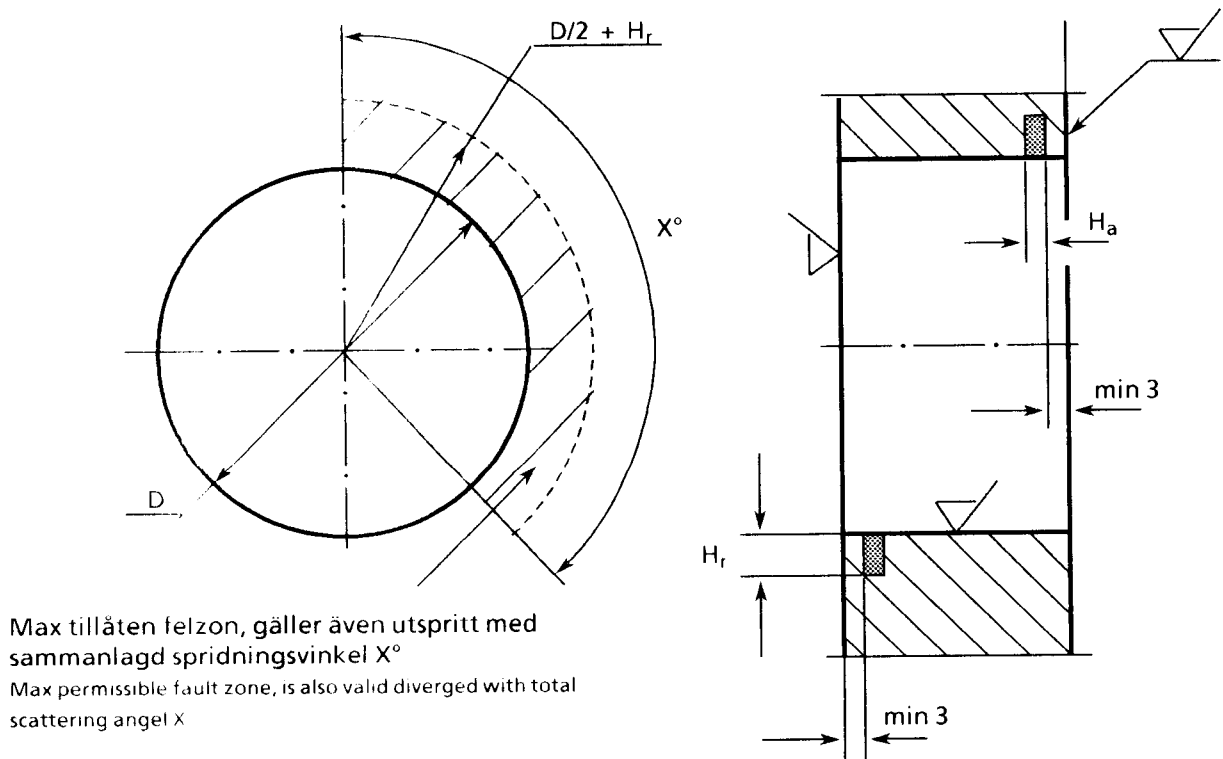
Inre defekter kring borrhål/Internal defects around drilled hole
